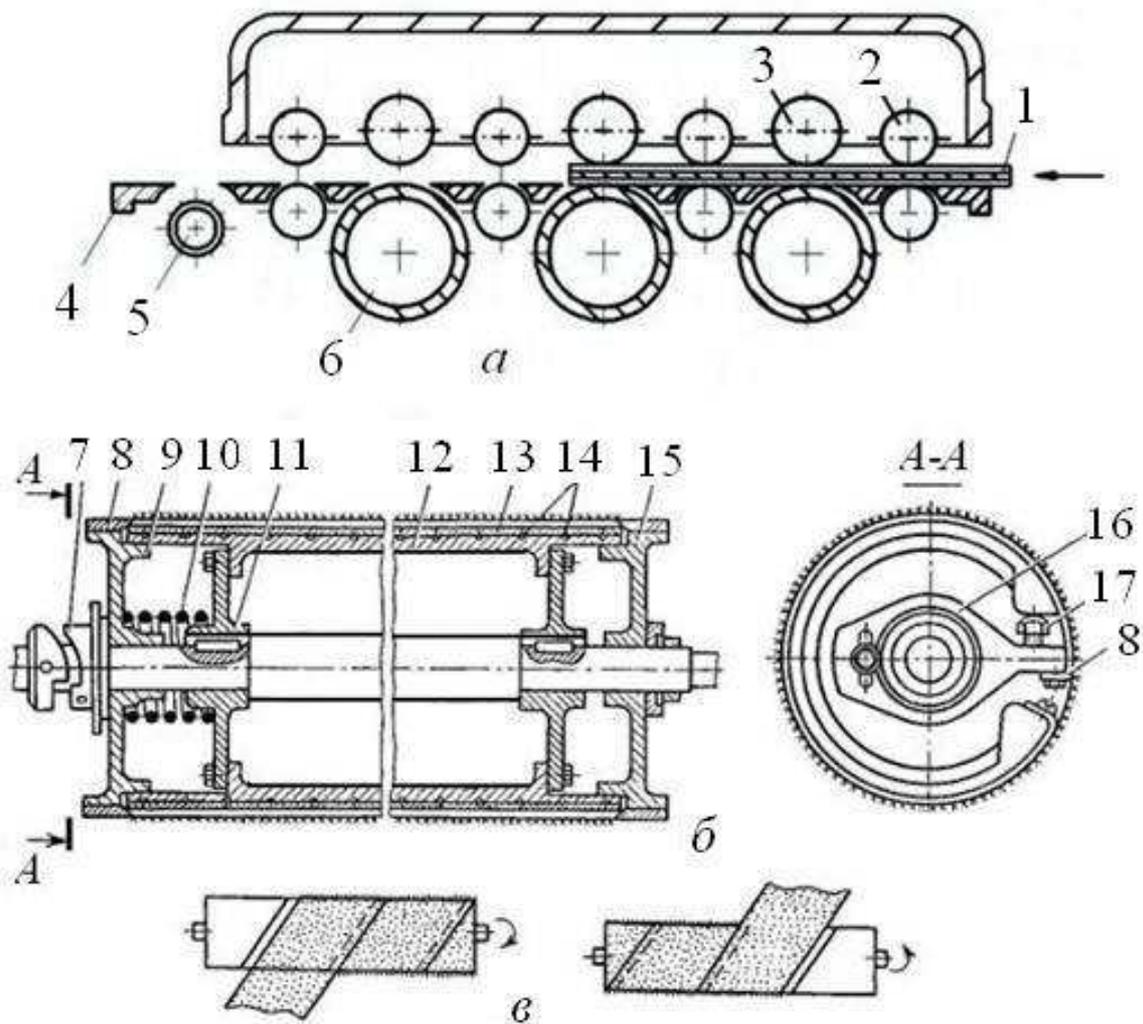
Шлифовальный широколенточный цилиндрический станок:
